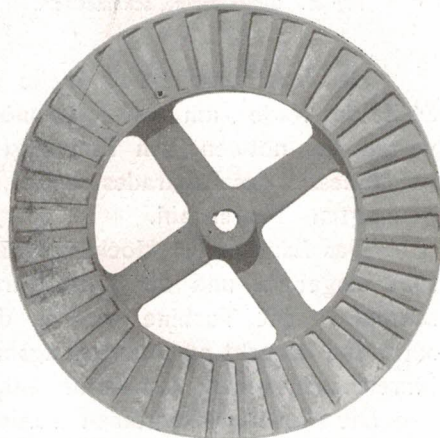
Laufrad einer Girard-Niederdruckturbine. Seite des Wasseraustrittes.
